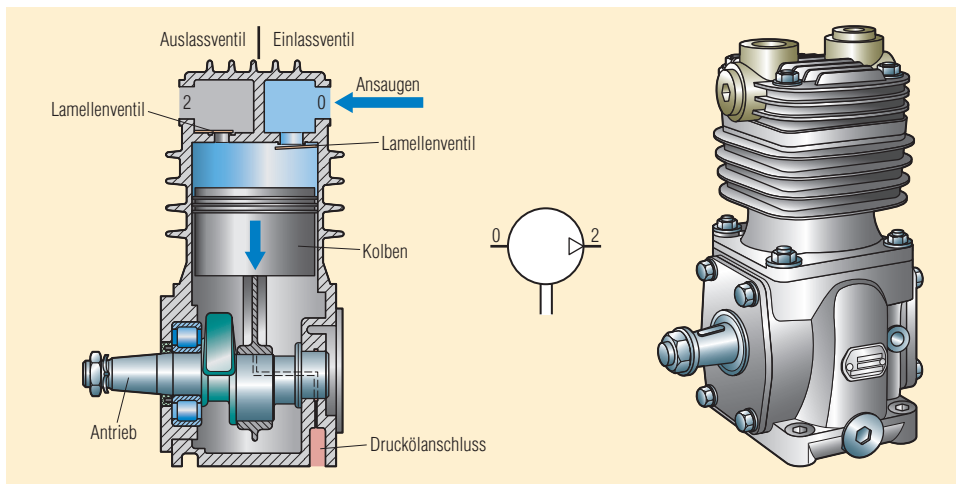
Kompressor mit Umlaufschmierung und Lamellenventilen.
